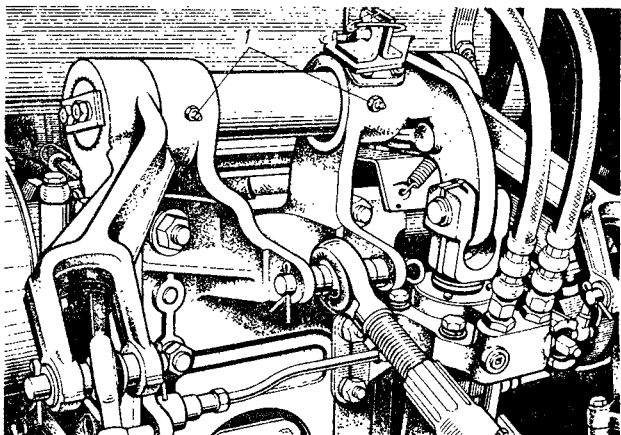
Смазывание втулок поворотного вала механизма навески:
